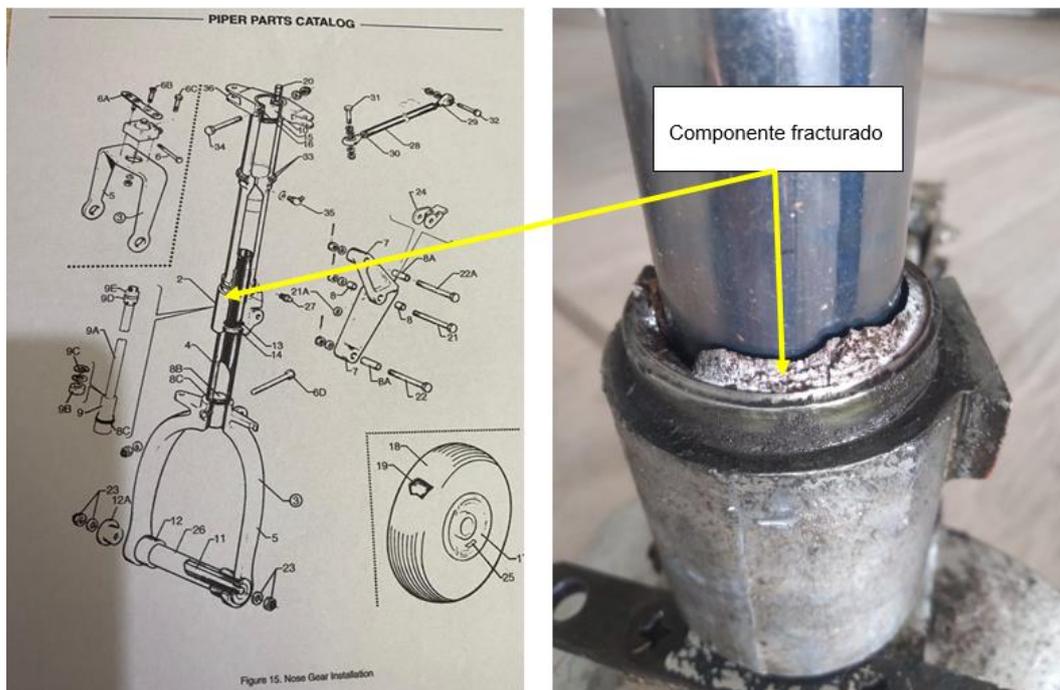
Pieza fracturada indicada en el catálogo de partes de la aeronave (*parts catalog PA-38-112⁴*) y su posición real en el tren de aterrizaje de nariz. Fuente: investigación JST
